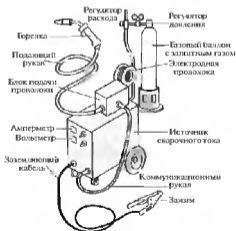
Установка для полуавтоматической сварки плавящимся электродом
